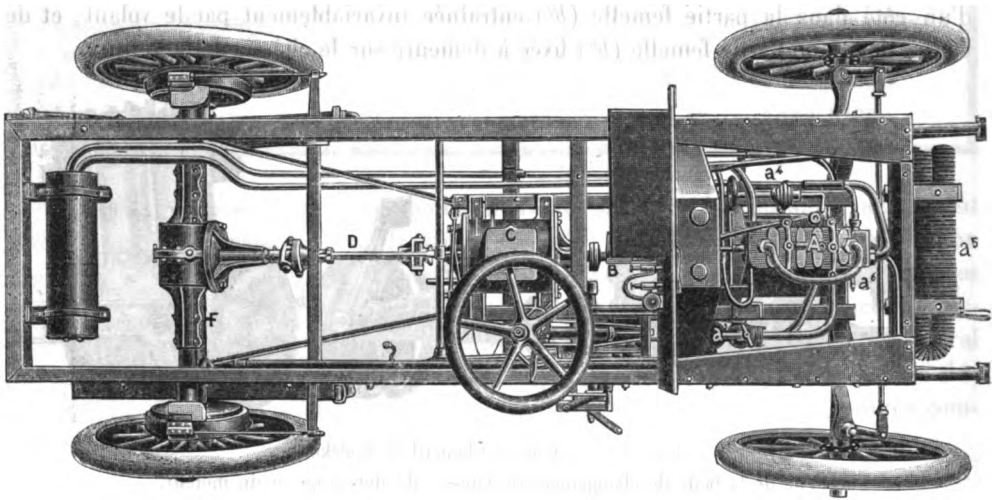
Vue en plan du châssis Chenard et Walcker.
